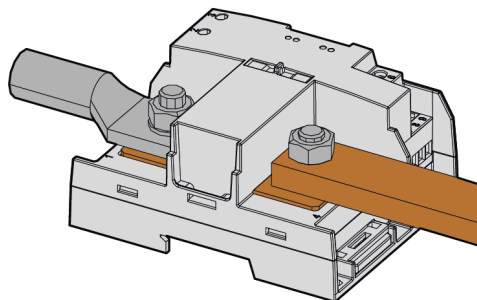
Vertikale Montage Schraubanschluss zu Leiste
